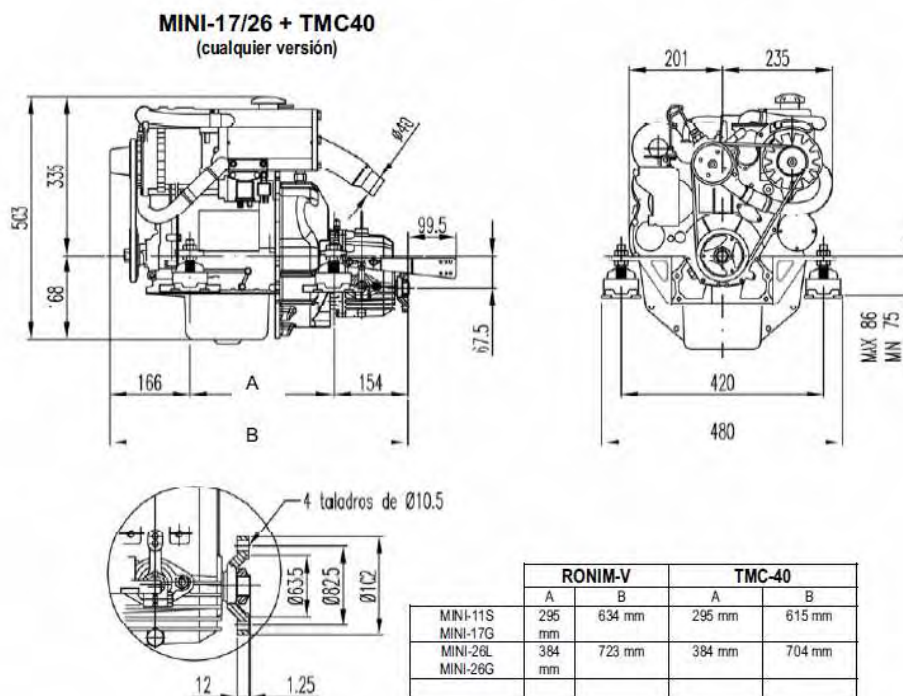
Dimensiones del motor MINI-17 y la reductora TMC40.
